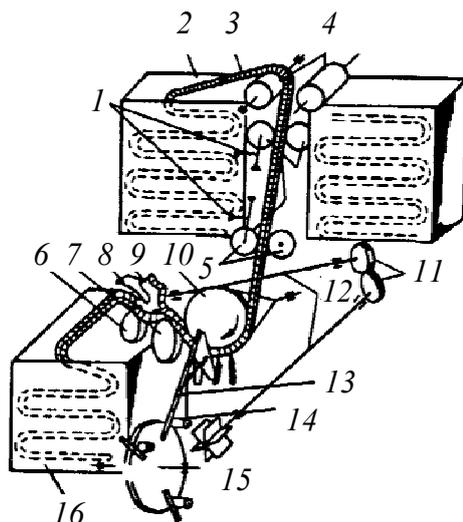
Схема лесопосадочного автомата: 1 – пружины; 2 – контейнер; 3 – кассетный сеянцедержатель; 4 – направляющий валик; 5 – ролик; 6, 7 – прижимные ролики; 8 – отсекатель; 9 – ведущая звездочка; 10 – ролик профильный; 11 – зубчатые колеса; 12 – вал привода; 13 – посадочный аппарат; 14 – упор; 15 – привод протяжки; 16 – контейнер с отработанной кассетой
